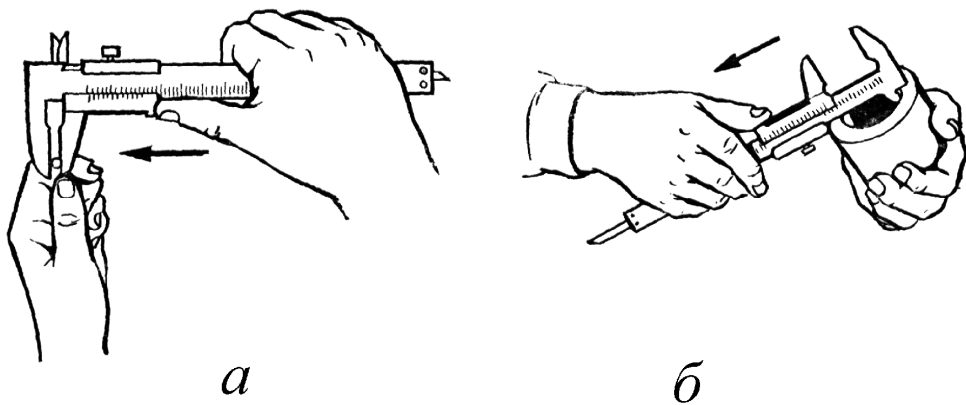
Измерение штангенциркулем наружных (а) и внутренних (б) размеров незакрепленной детали
